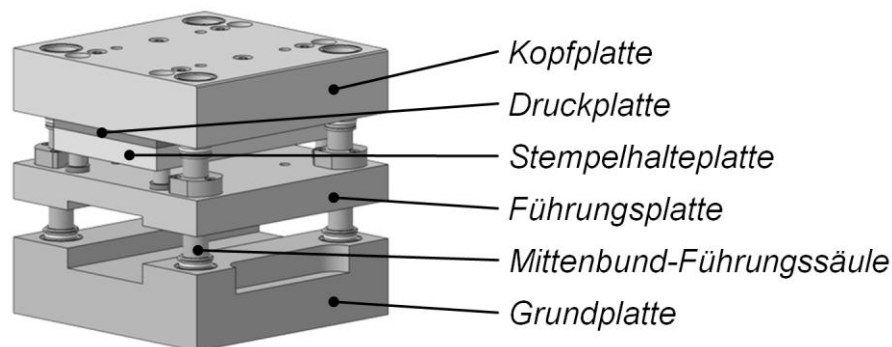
4-Säulen-Werkzeuggestell in massiver Ausführung [STRA11]
